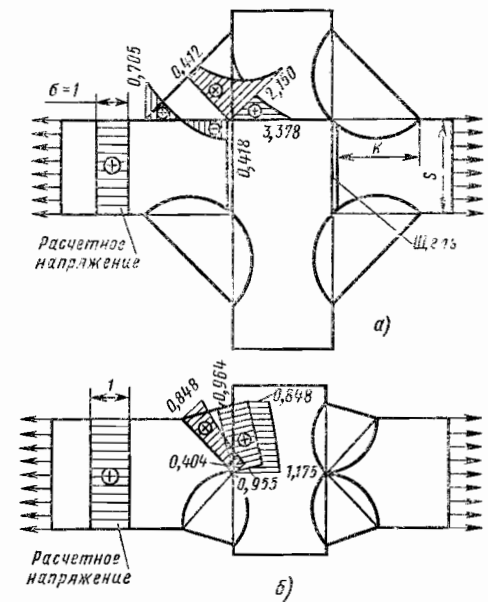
Напряжения в тавровом соединении: а — детали перед сваркой без скоса кромок; б — детали с двусторонним скосом кромок
